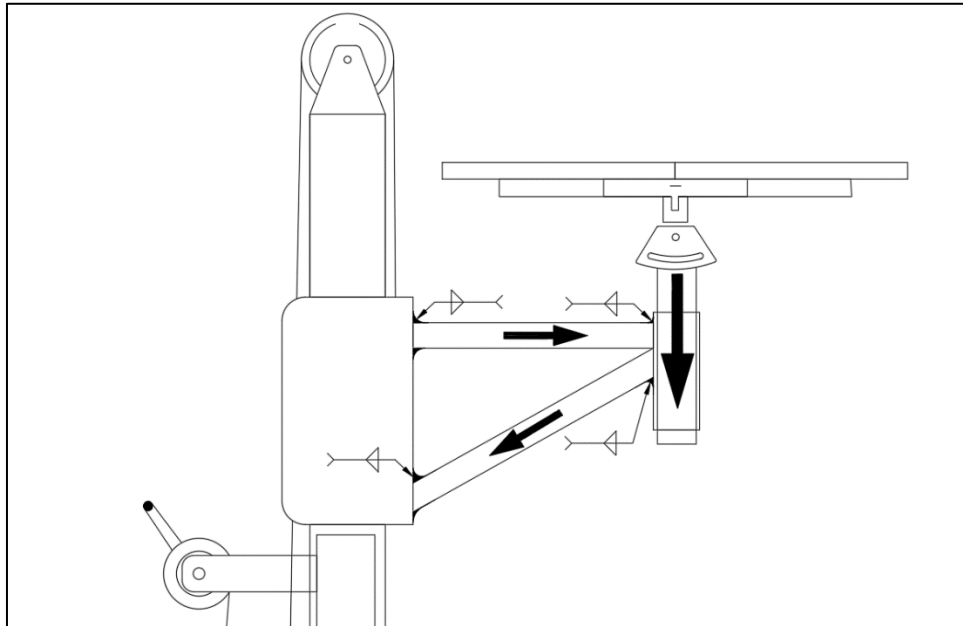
Uniones soldadas a filete existentes en el soporte de la plataforma.
